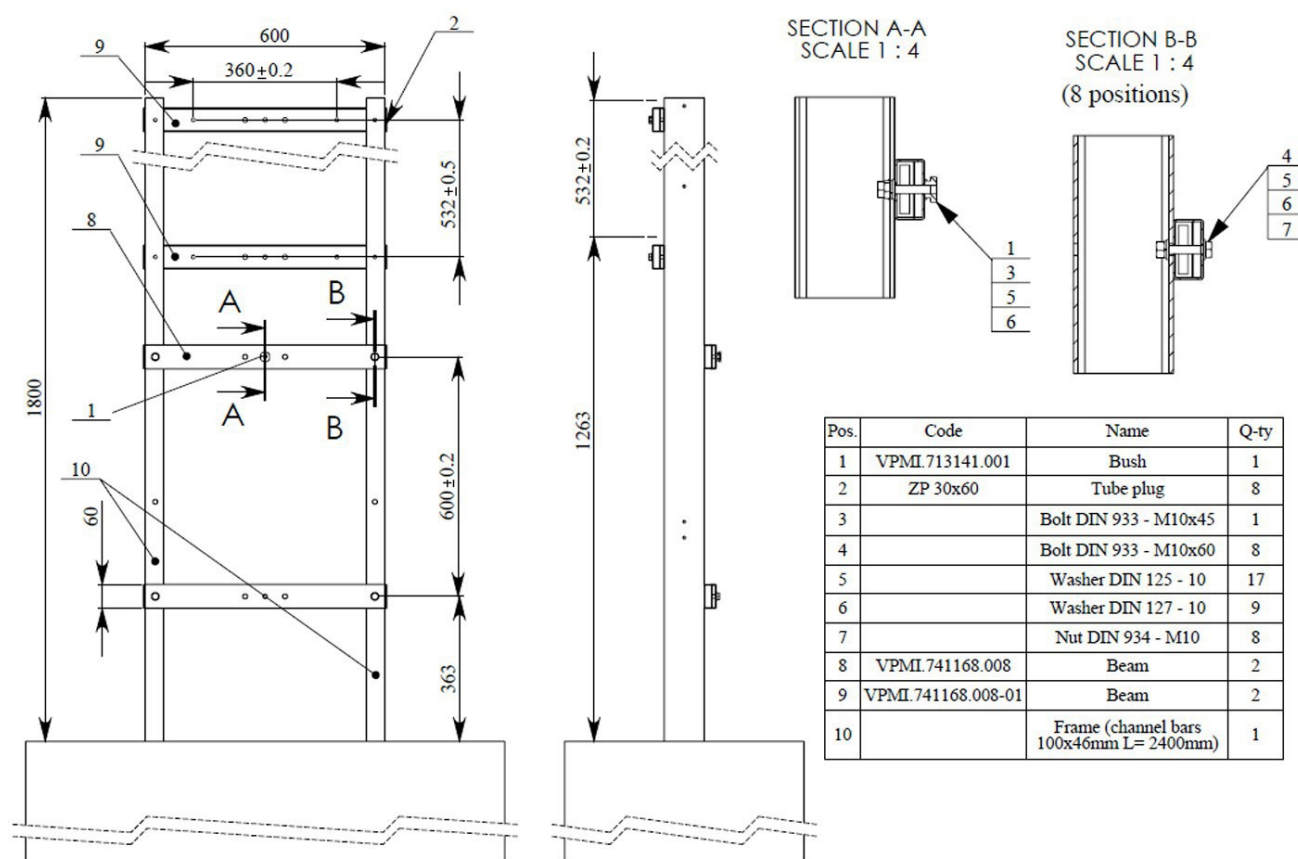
Montaje de vigas y casquillos en el pilar principal de PoliGate Light G2
